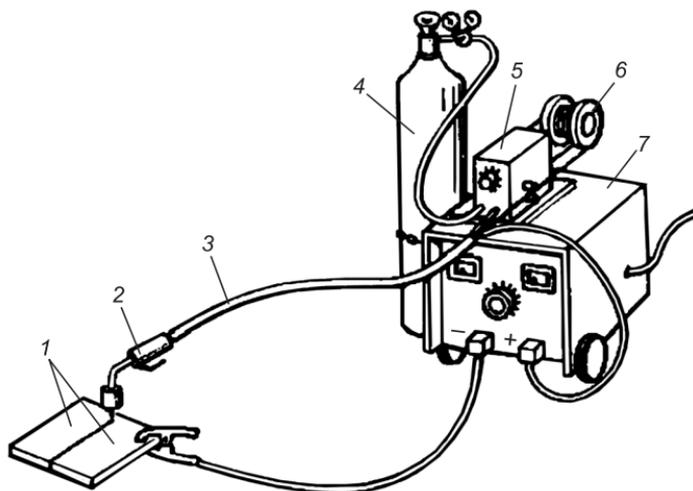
Сварочный пост механизированной дуговой сварки плавящимся электродом
